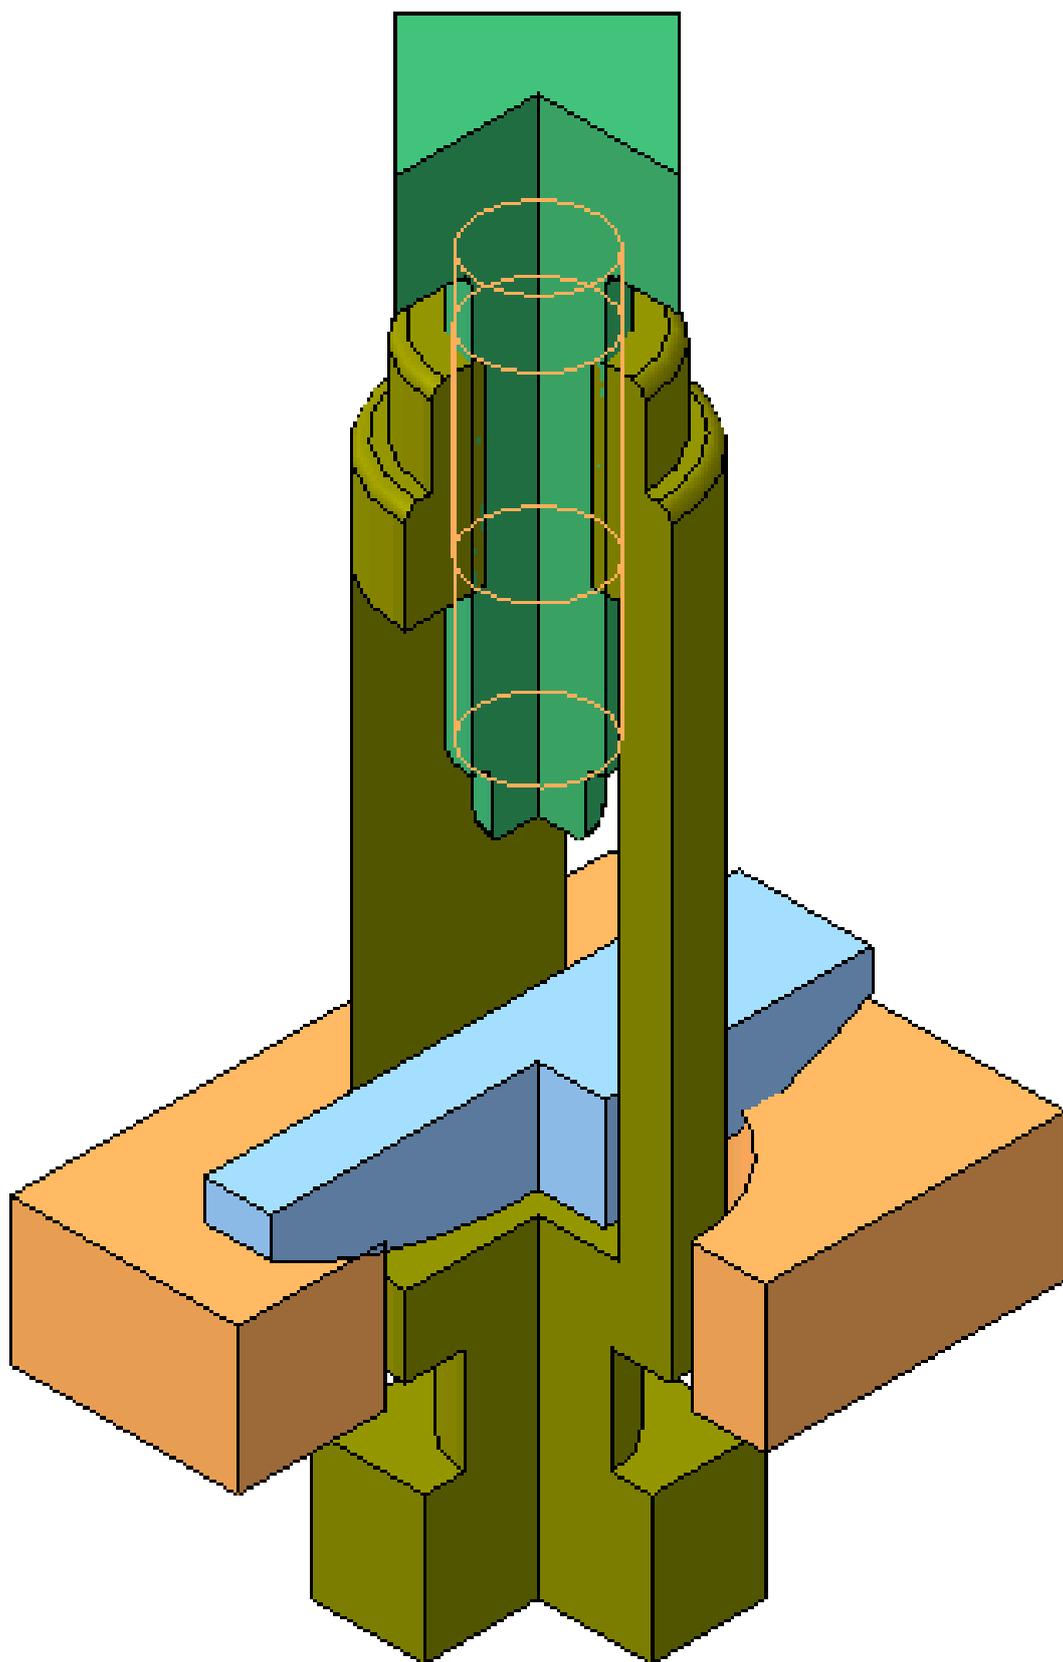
3D-модель сборки изделия «Резцедержатель» (варианты 15, 35)
